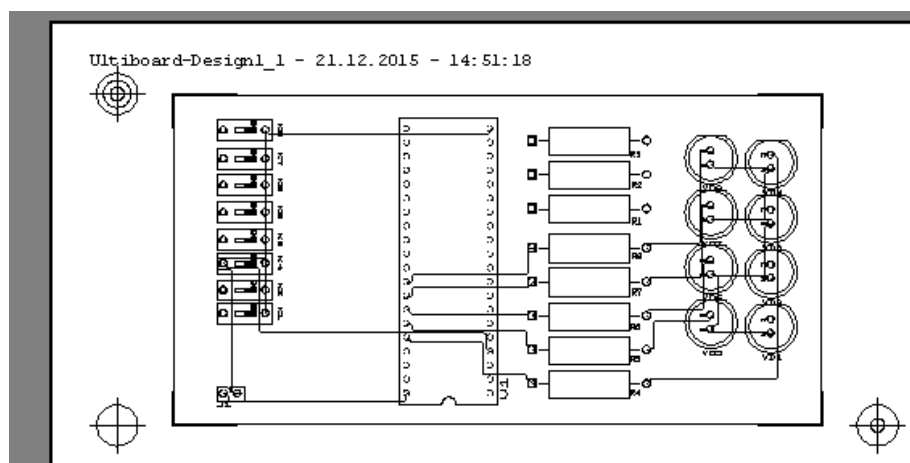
Верхний слой двухслойной печатной платы РЭС
